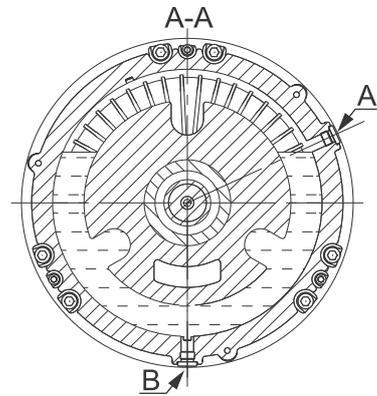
Comprobación del nivel de líquido de motor con la bomba en posición horizontal
